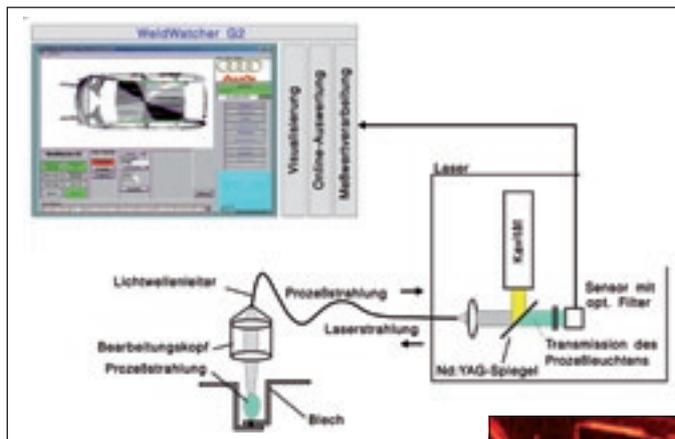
Beispiel eines In-Process Sensors im Laseraggregat beim Laserschweißen
